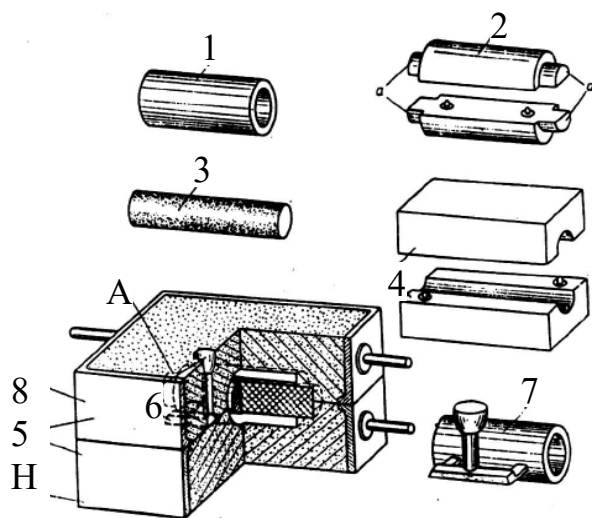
Схема лиття у піщано-глиняні форми: 1 – заготівка; 2 – модель; 3 – стержень; 4 – форма для одержання стержня; 5 – основна ливарна форма; 6 – ливникова система; 7 – виливок
